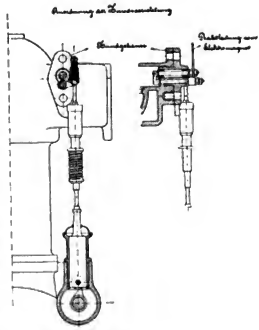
Marienfelder Daimler-Petroleum-Schiffsmotor mit Gemisch-Regulierung.
